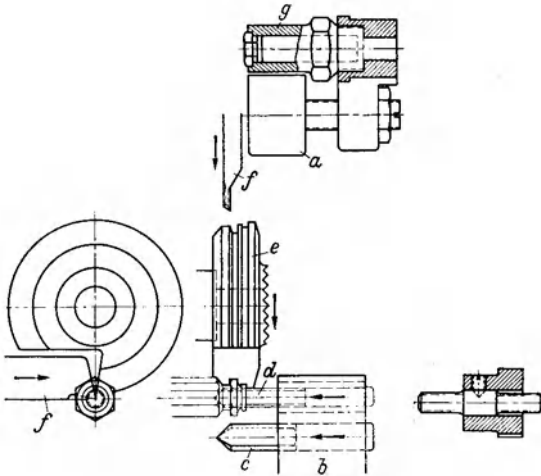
Bearbeitung einer Messingmutter mit Gewinde. *a* Anschlag im Greifarm; *b* Stahlhalter für zwei Bohrwerkzeuge im Langdrehschlitten; *c* Anbohrer; *d* Flachbohrer; *e* Formstahl auf dem hinteren Querschlitten; *f* Abstechstahl von oben; *g* Aufnahmebüchse im Greifarm zum Abnehmen und Abführen des Teiles in einen getrennten Behälter.
